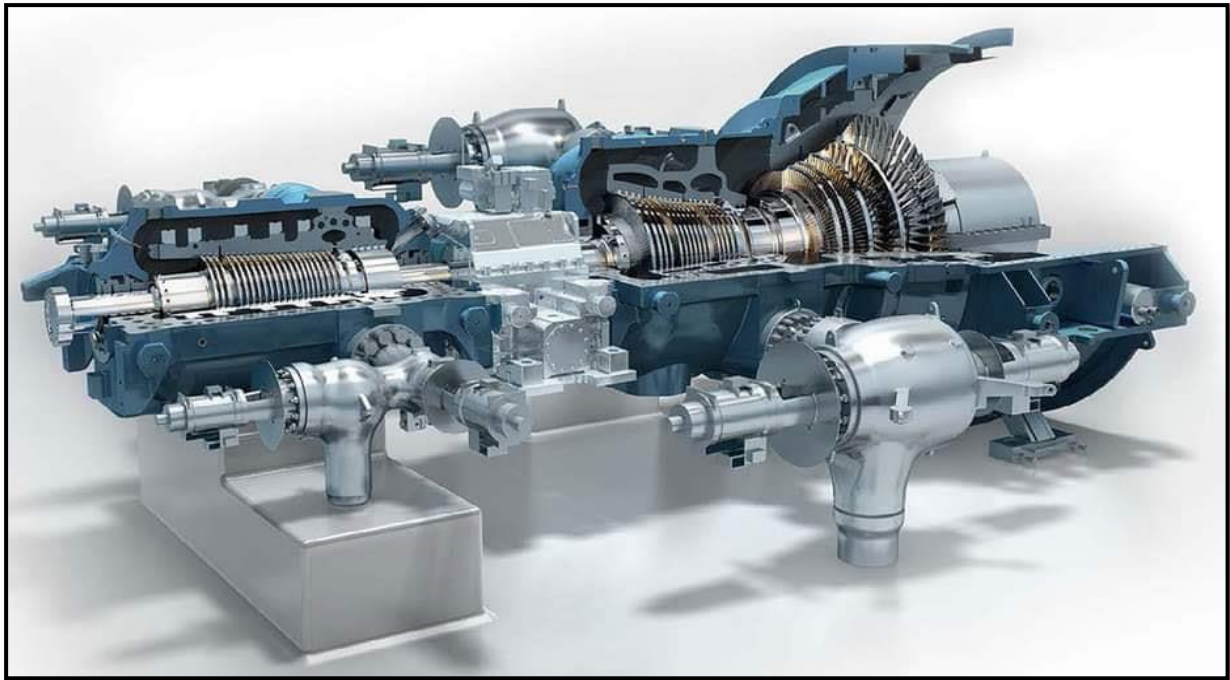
Vue d'ensemble turbine TV SST5-3000
